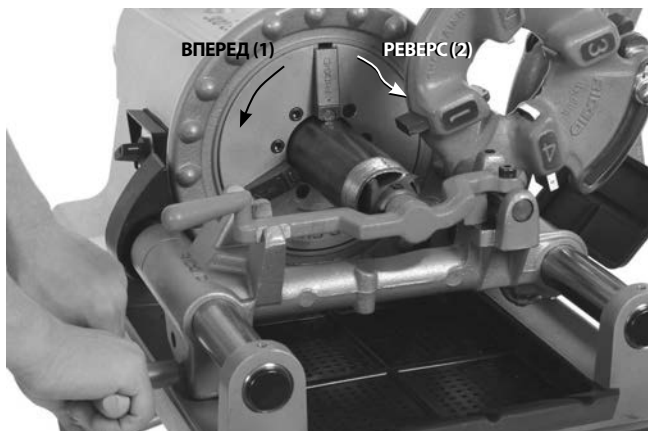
Зенкование трубы с помощью зенковки, вращение станка
